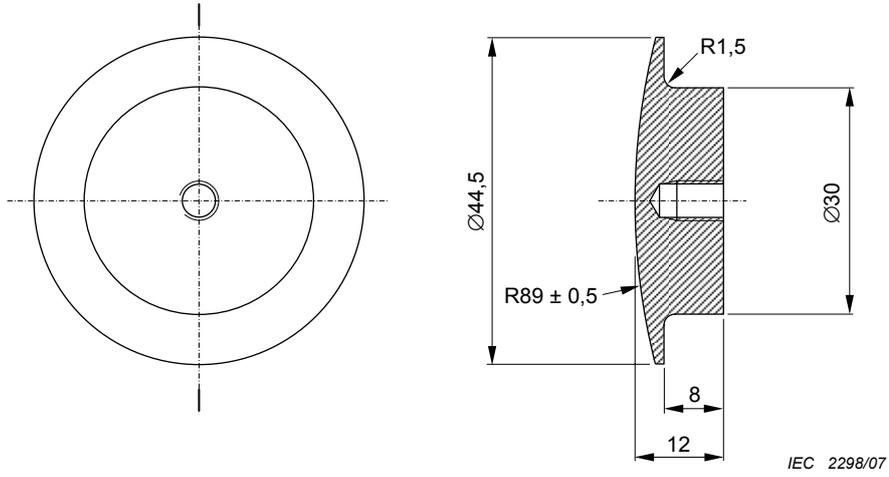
Dimensions de la base de l'élément d'impédance mécanique
